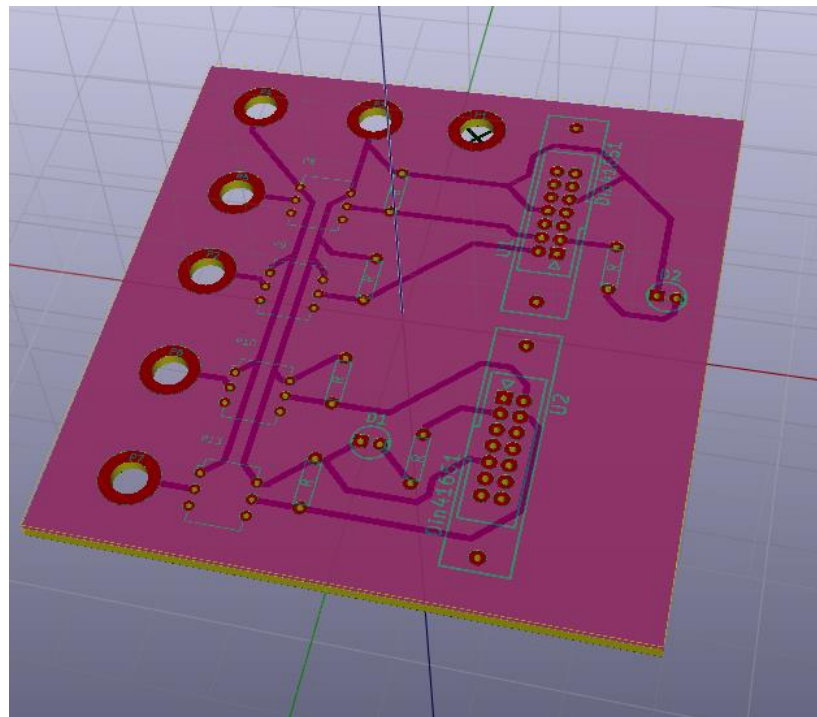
PCB Acoplamiento a Driver – Salidas en 3D
